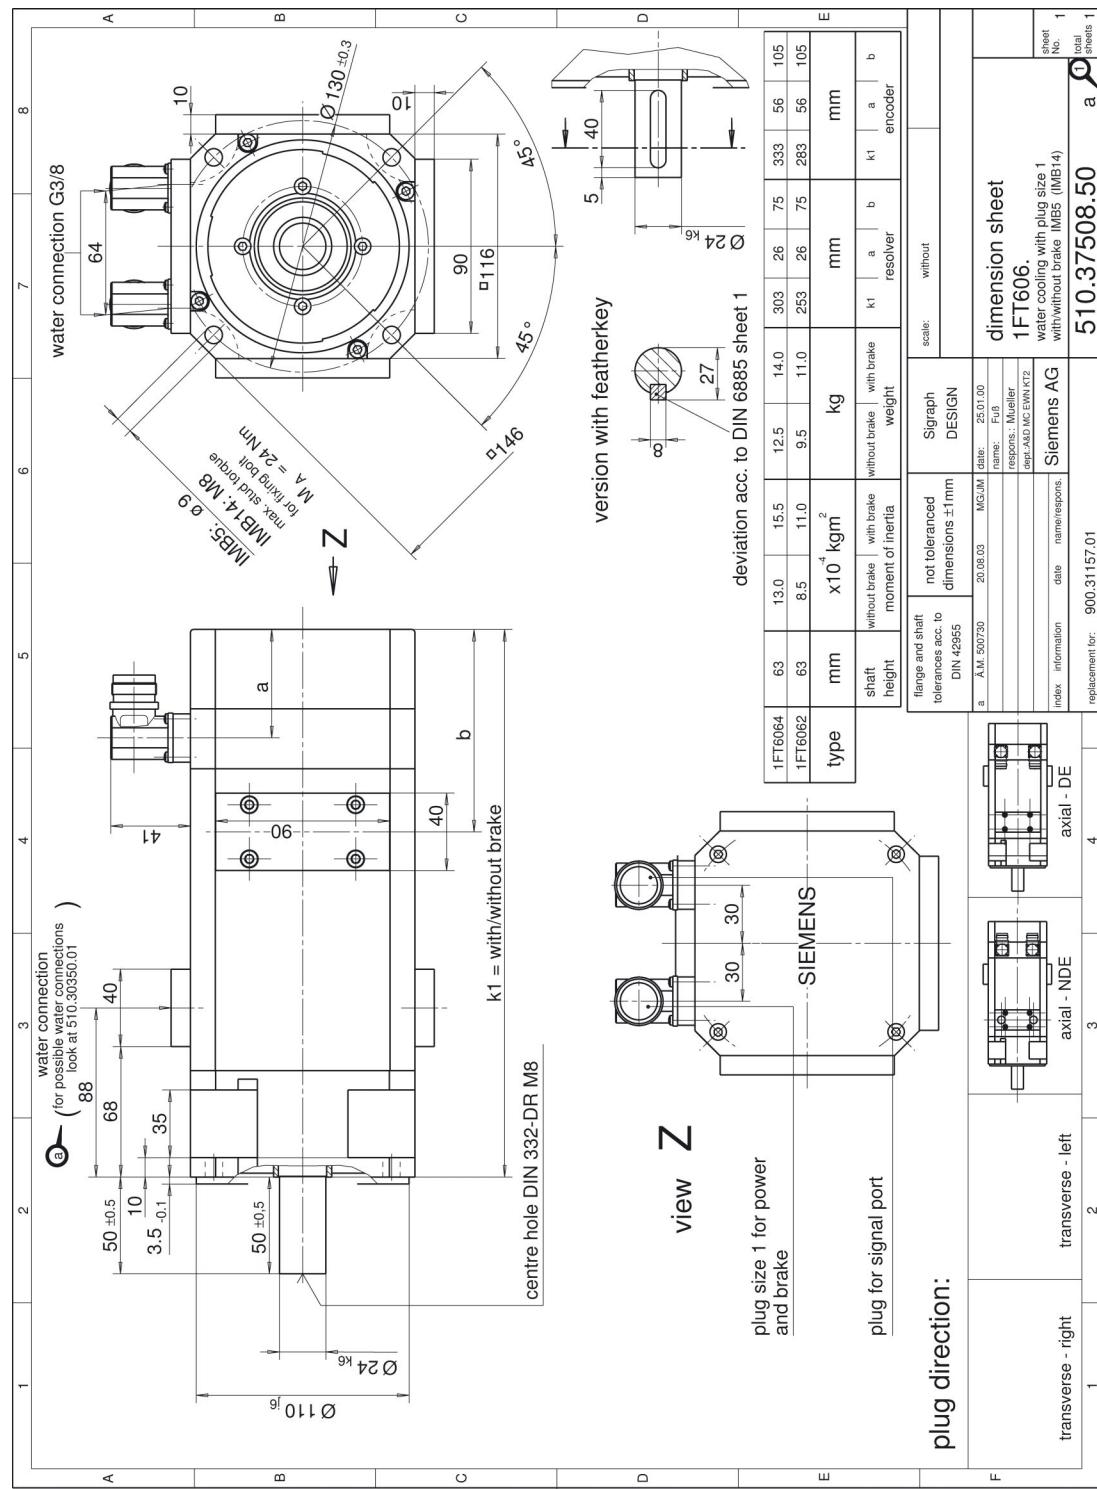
1FT606□ wassergekühlt mit Stecker Größe 1
